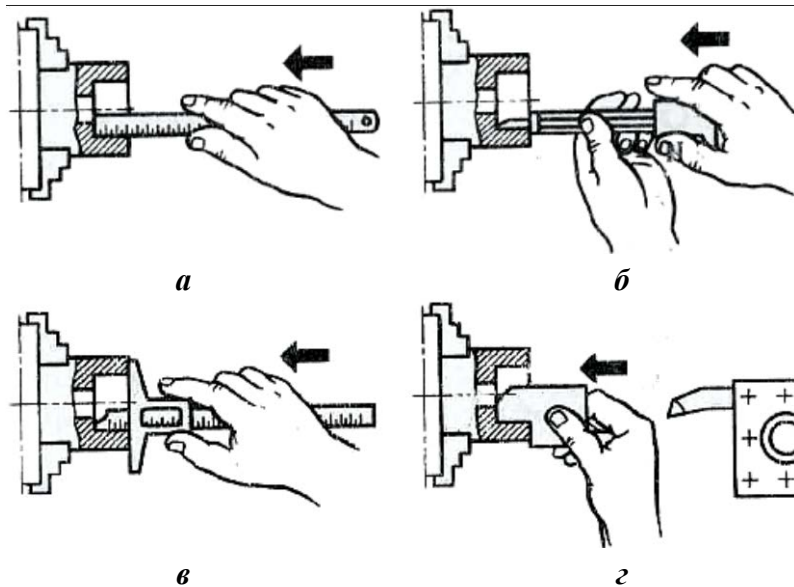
Вимірювання довжини від торця заготовки до уступу
